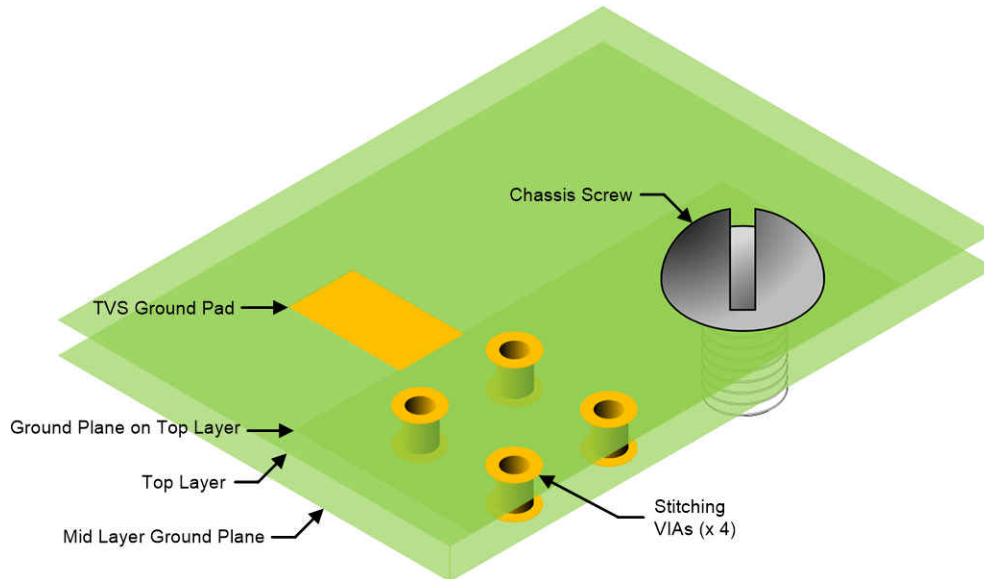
两层 PCB - 顶层接地平面缝合到中间层接地平面
